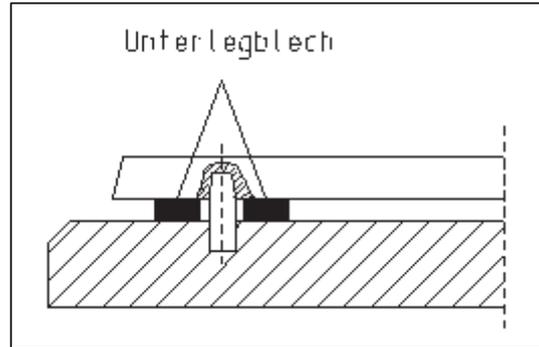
Befestigungsmaterial für Pumpe mit freiem Wellenende
